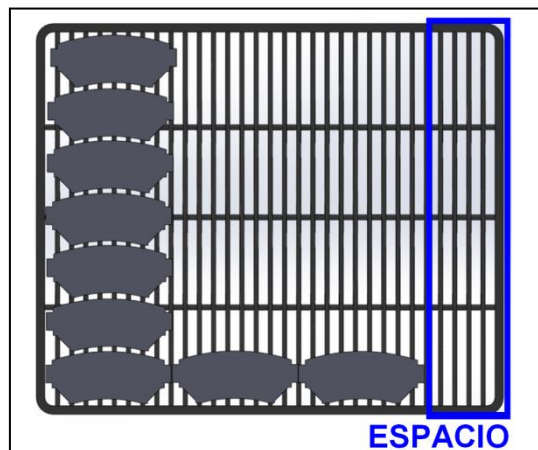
Espacio sobrante una vez calculado las pastillas de largo y ancho que caben.
